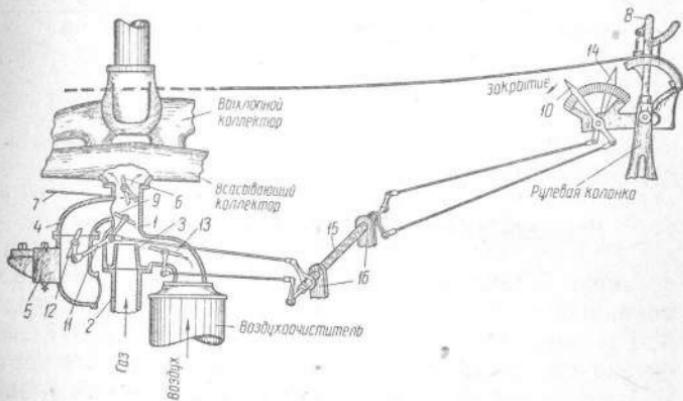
Смеситель двигателя трактора «сталинец-60»
